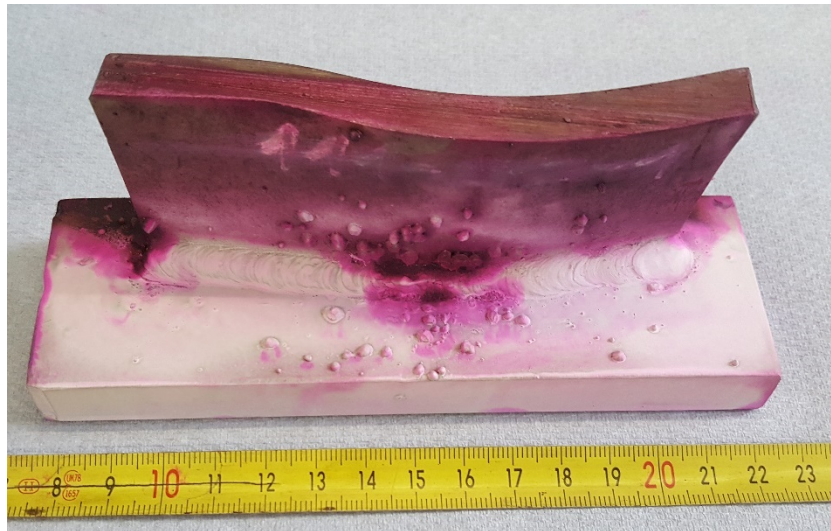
Schweißprobe 111-012-1; Verbund aus Altstahl und S235 JR, Eindringprüfung (PT)
